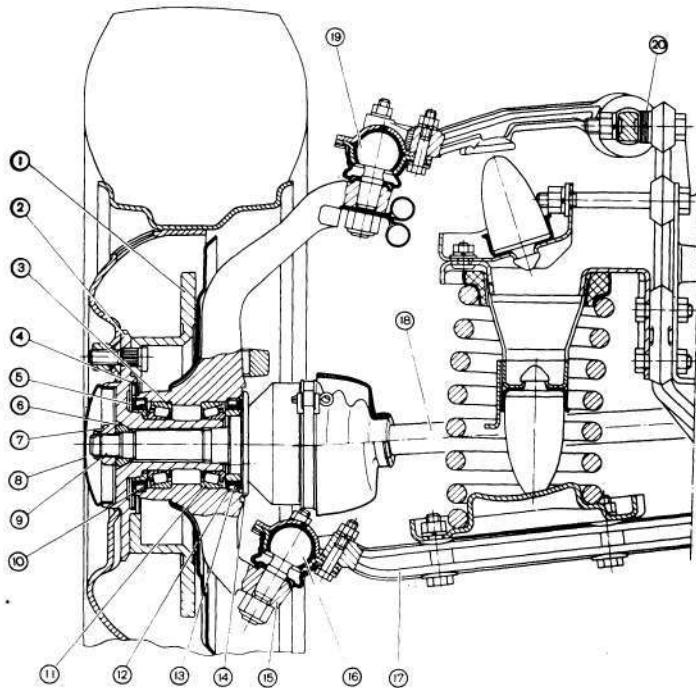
Переднее колесо: 1 — тормозной диск; 2 — ступица; 3 — наружный роликовый подшипник; 4 — защитное кольцо наружного сальника; 5 — наружный сальник; 6 — конусная втулка; 7 — гайка крепления ступицы; 8 — колпак ступицы; 9 — хвостовик карданного вала; 10 — демонтажное кольцо наружного сальника; 11 — внутренний роликовый подшипник; 12 — демонтажное кольцо внутреннего сальника; 13 — внутренний сальник; 14 — защитное кольцо внутреннего сальника; 15 — поворотный кулак; 16 — шаровая опора нижнего рычага; 17 — нижний рычаг; 18 — карданный вал; 19 — шаровая опора верхнего рычага; 20 — набор прокладок
